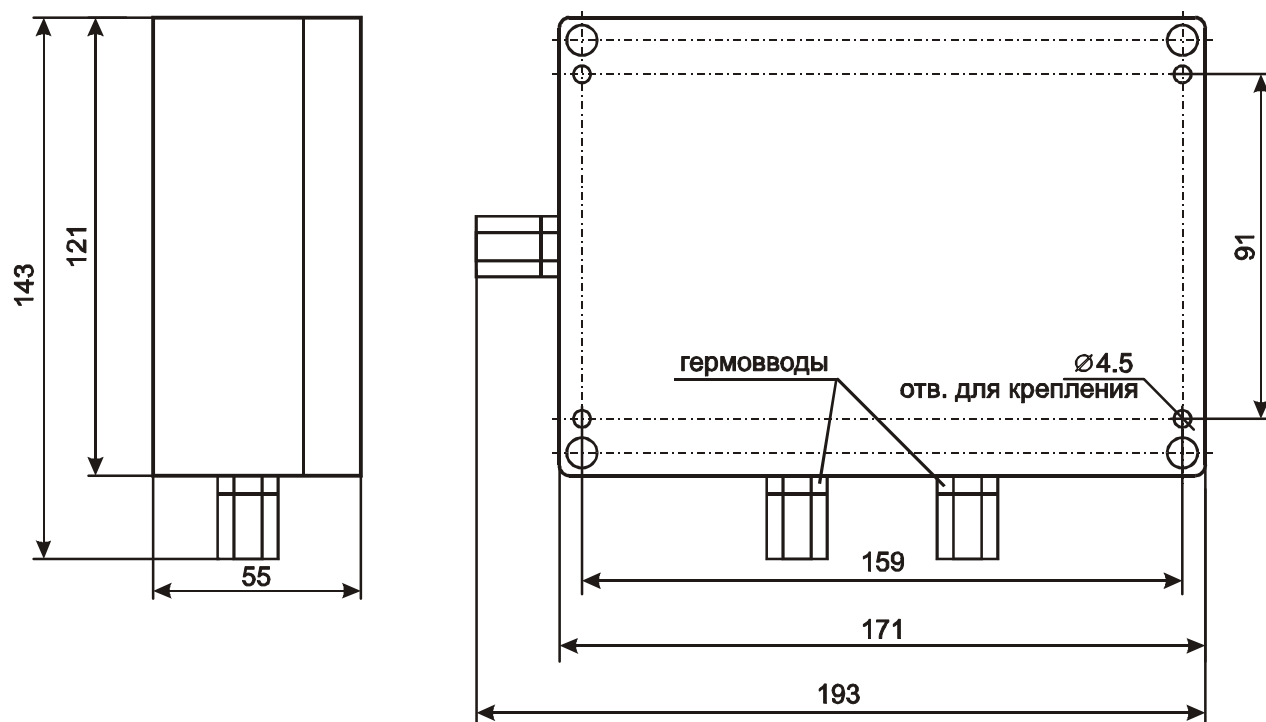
Внешний вид и габаритные размеры БРЛ в исп. IP65
